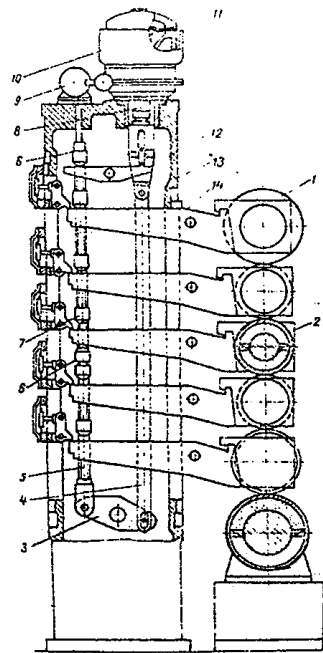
Машинний каландр: 1 – металеві вали; 2 – корпус підшипника; 3 – коромисло вилегчування валів; 4 – сполучні тяги; 5 – тяги підйому і притиску валів; 6 – упори притиску валів; 7 – упори підйому і притиску валів; 8 – гвинти підйому валів; 9 – електродвигун механізму підйому валів; 10 – черв’ячний редуктор підйому валів; 11 – діафрагма притиску валів; 12 – коромисло притиску валів; 13 – станина; 14 – важелі валів
